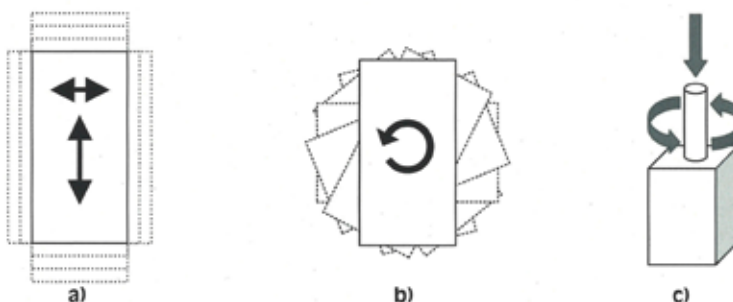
Esquisses de principe pour le soudage linéaire a) le soudage orbital b) et rotatif c)
